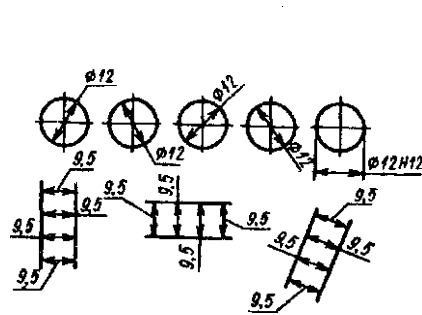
Нанесение размерного числа при короткой размерной линии
